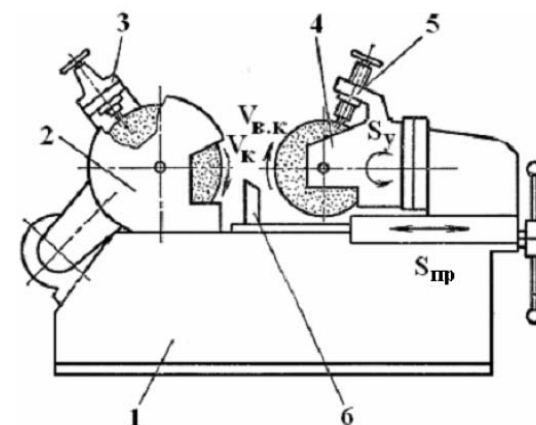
Бесцентрово-шлифовальный станок: 1 – станина; 2, 4 – бабки; 3, 5 – механизмы для правки кругов; 6 – нож
